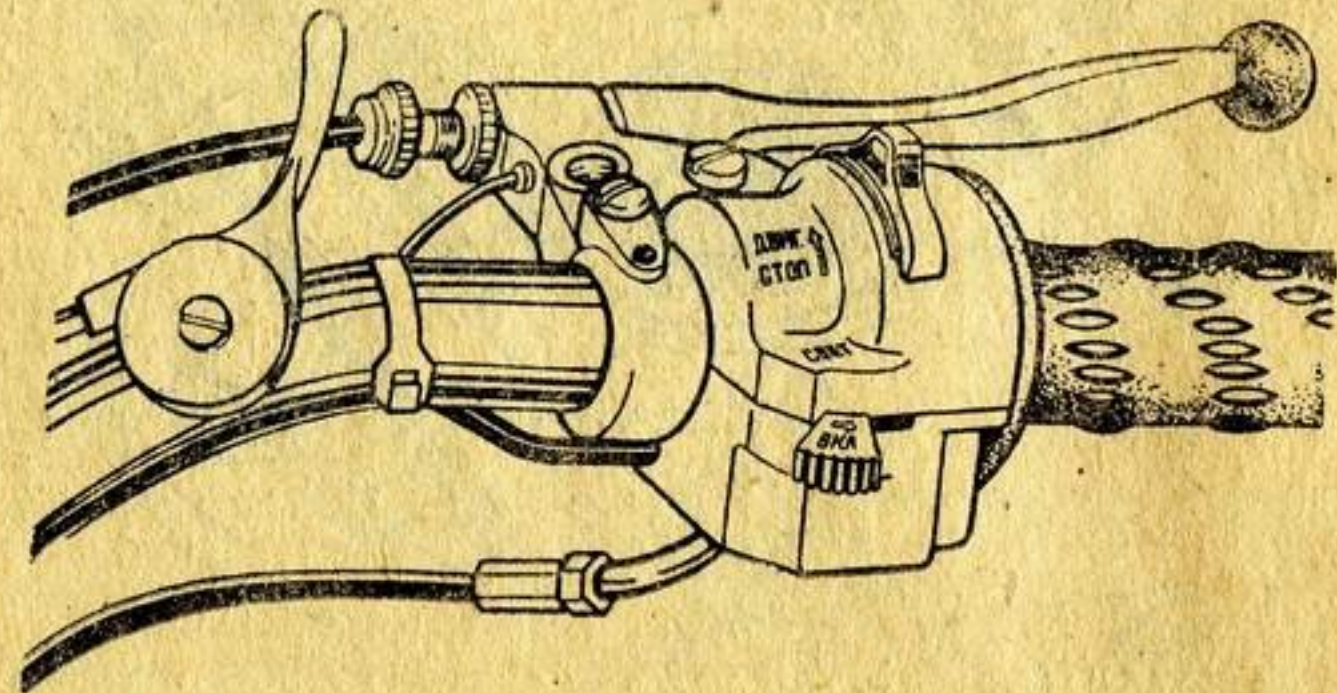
Включатель света, аварийный выключатель зажигания и рычаг топливного корректора
